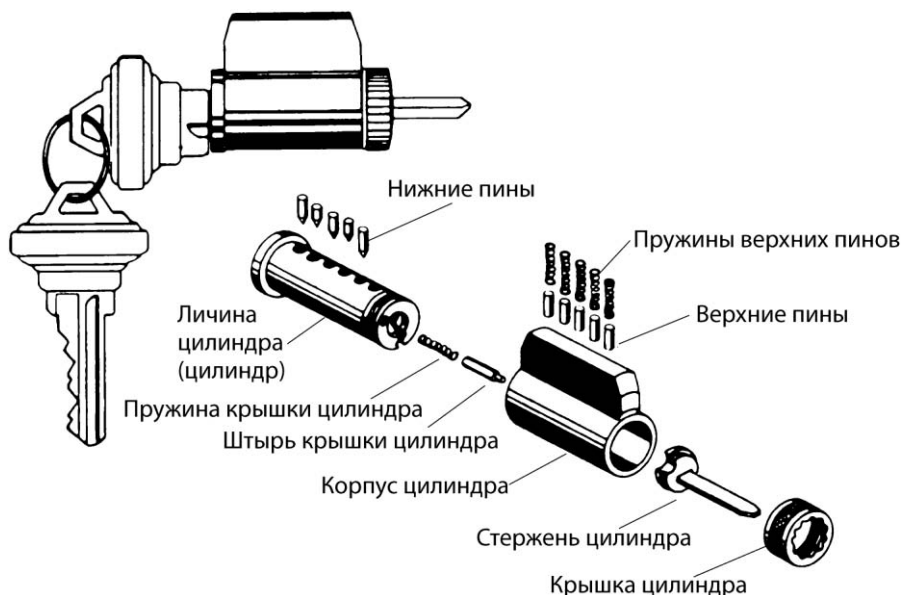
Детали пинового цилиндра для ручки-кнопки
